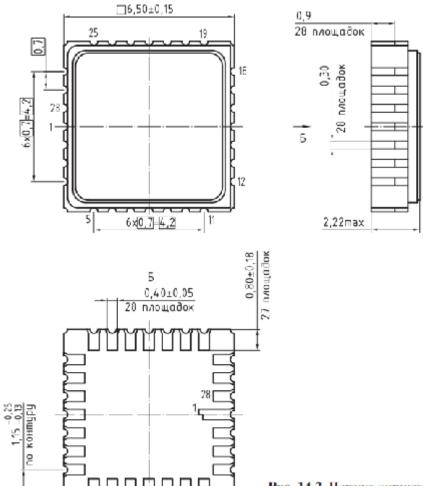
Чертеж корпуса МК 5123.28-1.01
